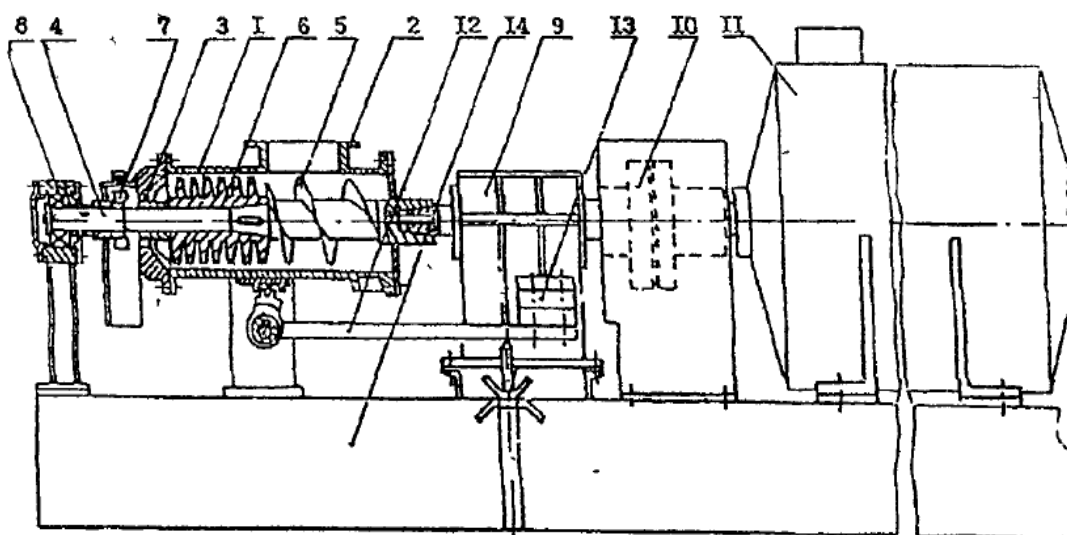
Схема фротапульпера: 1-корпус; 2-патрубок; 3-кольцевая щель; 4-валы; 5-заходный шнек; 6- рабочий шнек; 7- вертушка; 8- подшипниковая опора; 9- редуктор; 10- муфта; 11- электродвигатель; 12- механизм присадки; 13- груз; 14- рама.
